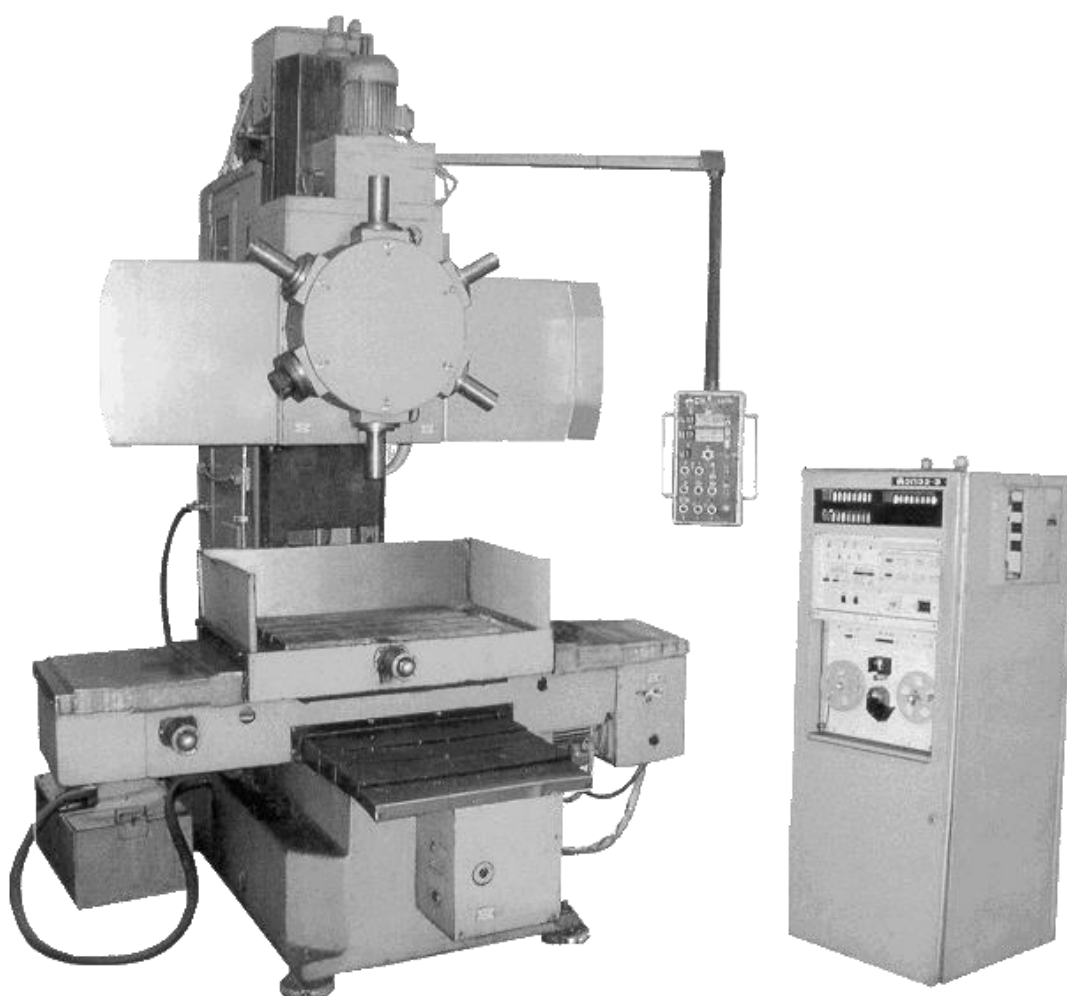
Свердлильний верстат з ЧПУ 2P135Ф2
